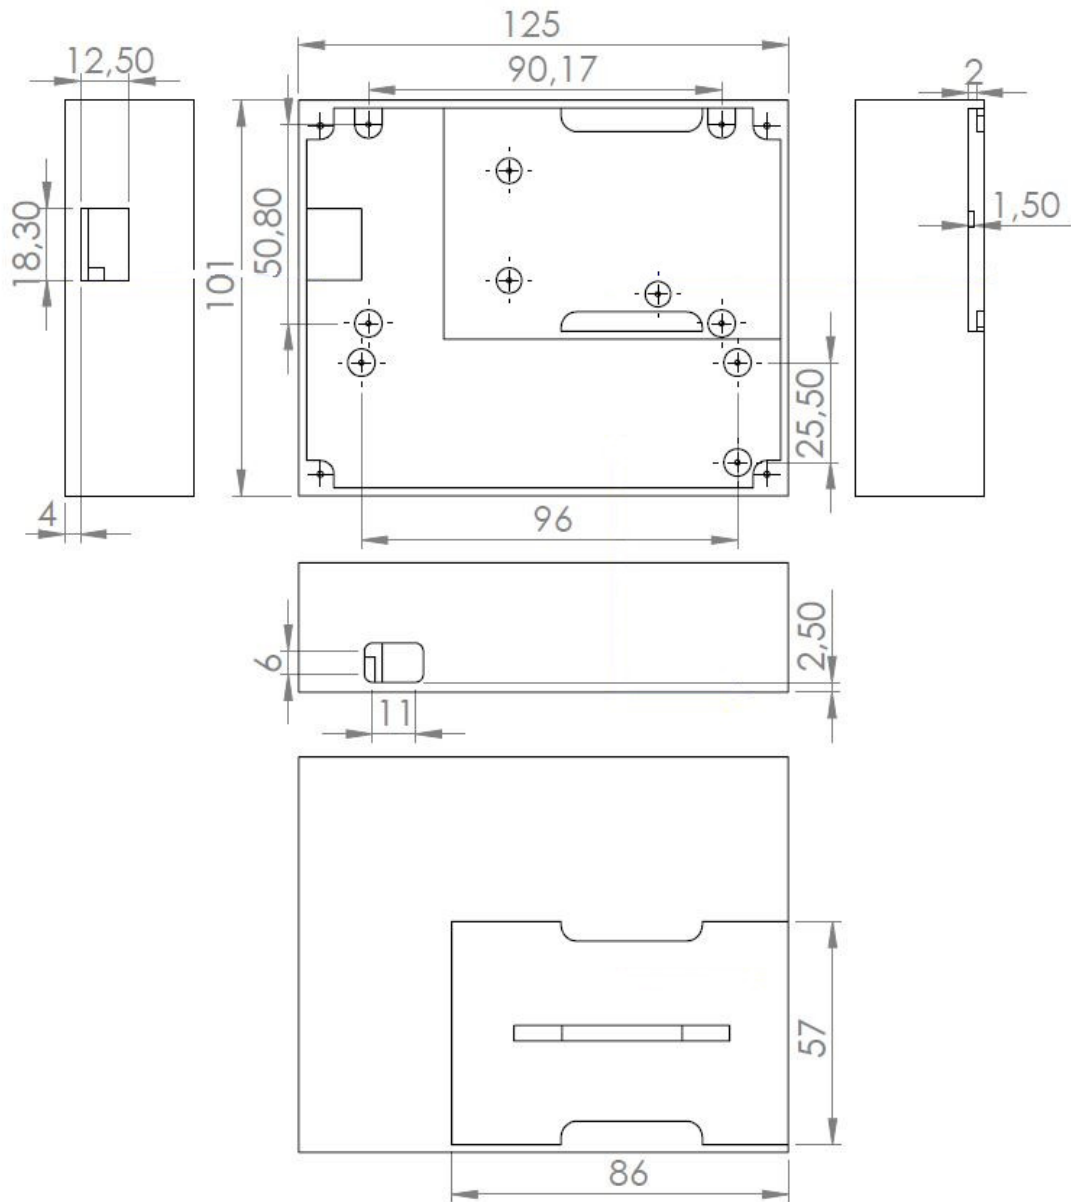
Desenho técnico da caixa (dimensões em mm) do terminal individual.
